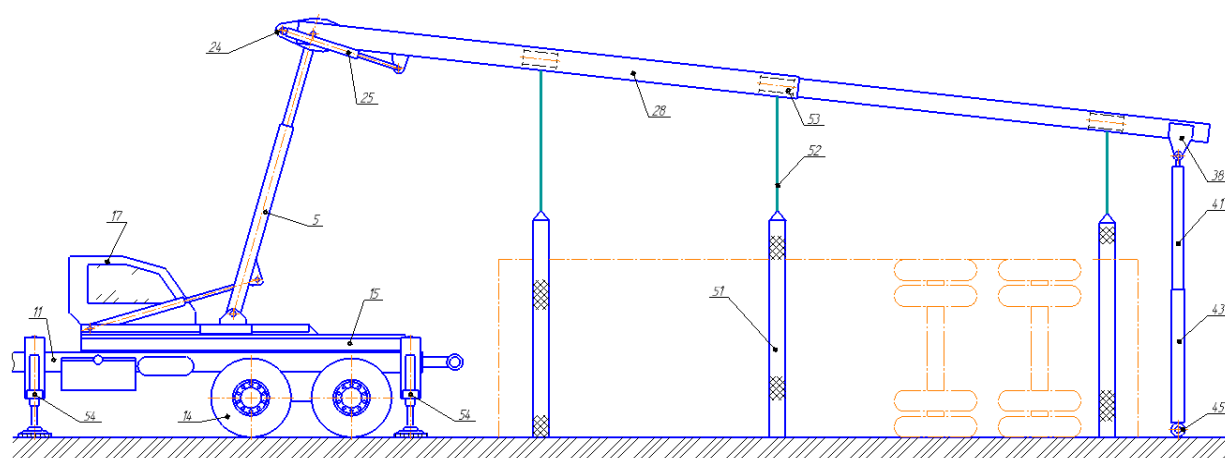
Аварийно-спасательный агрегат в рабочем положении
